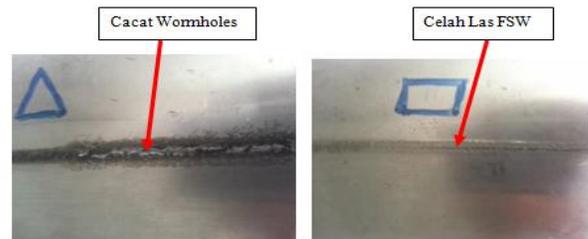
Spesimen Uji standar ASTM E08 hasil pengelasan FSW
